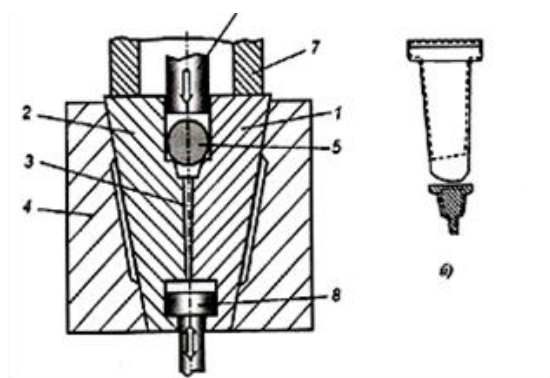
Принципиальная схема высокоскоростного выдавливания (а) и получаемой заготовки (б): 1, 2 – разъемные элементы матрицы; 3-ручей; 4-корпус; 5- исходная заготовка; 6- деформирующий боёк; 7- прижим
